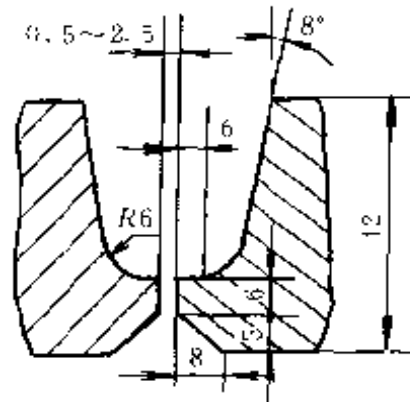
电站锅炉主焊缝对接坡口的形状及尺寸
